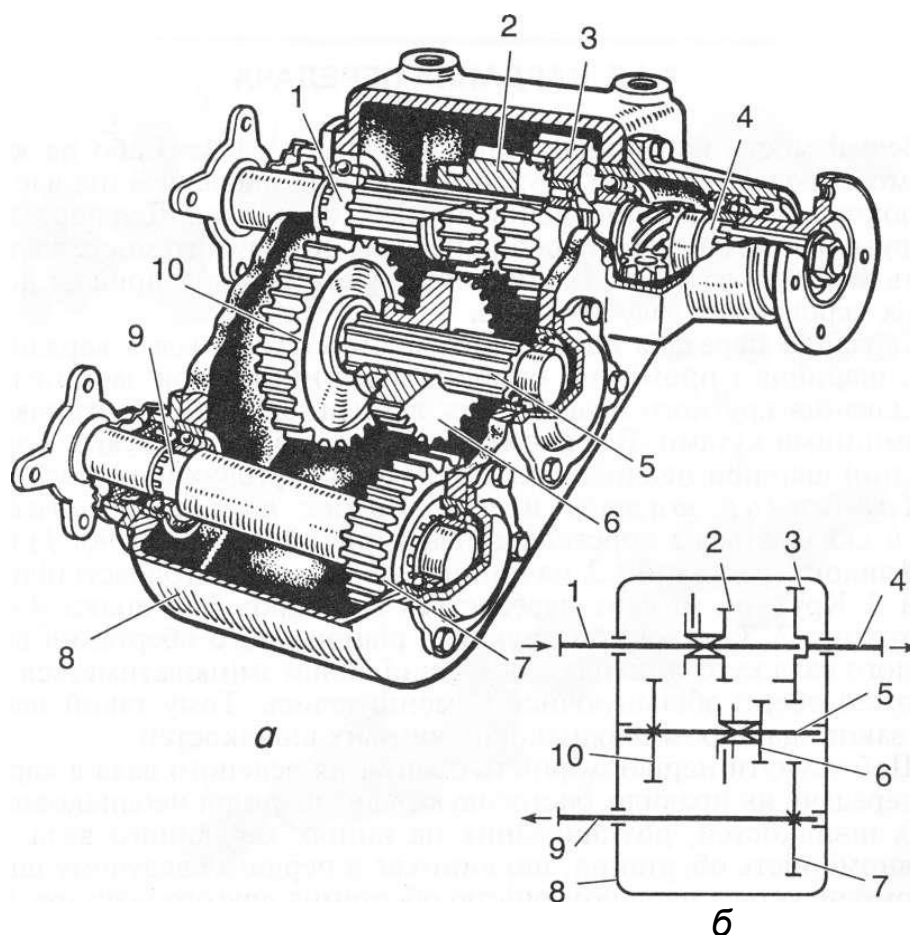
Роздавальна коробка з прямою та знижувальною передачами: а – загальний вигляд; б – кінематична схема; 1 – ведучий вал; 2, 3, 6, 7, 10 – шестерні; 4 – ведений вал; 5 – проміжний вал; 8 – корпус; 9 – вал привода передньою моста
